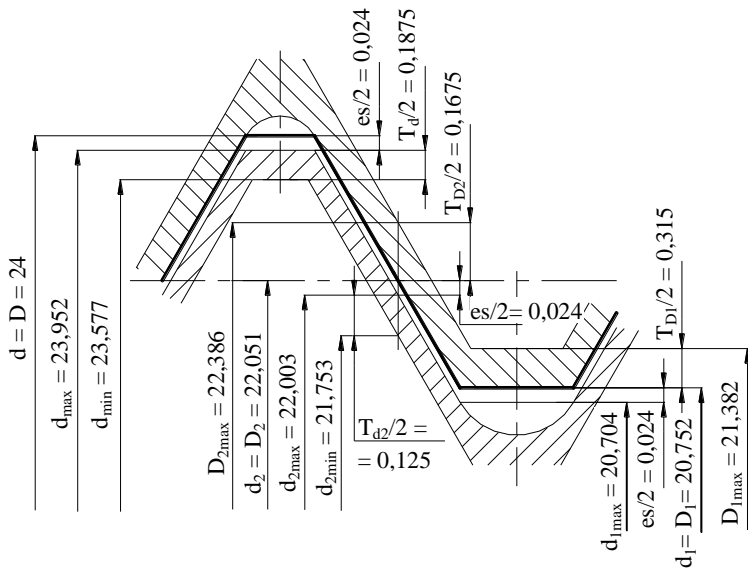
Поля допусків різьбового з'єднання M24 7H/7g6g
